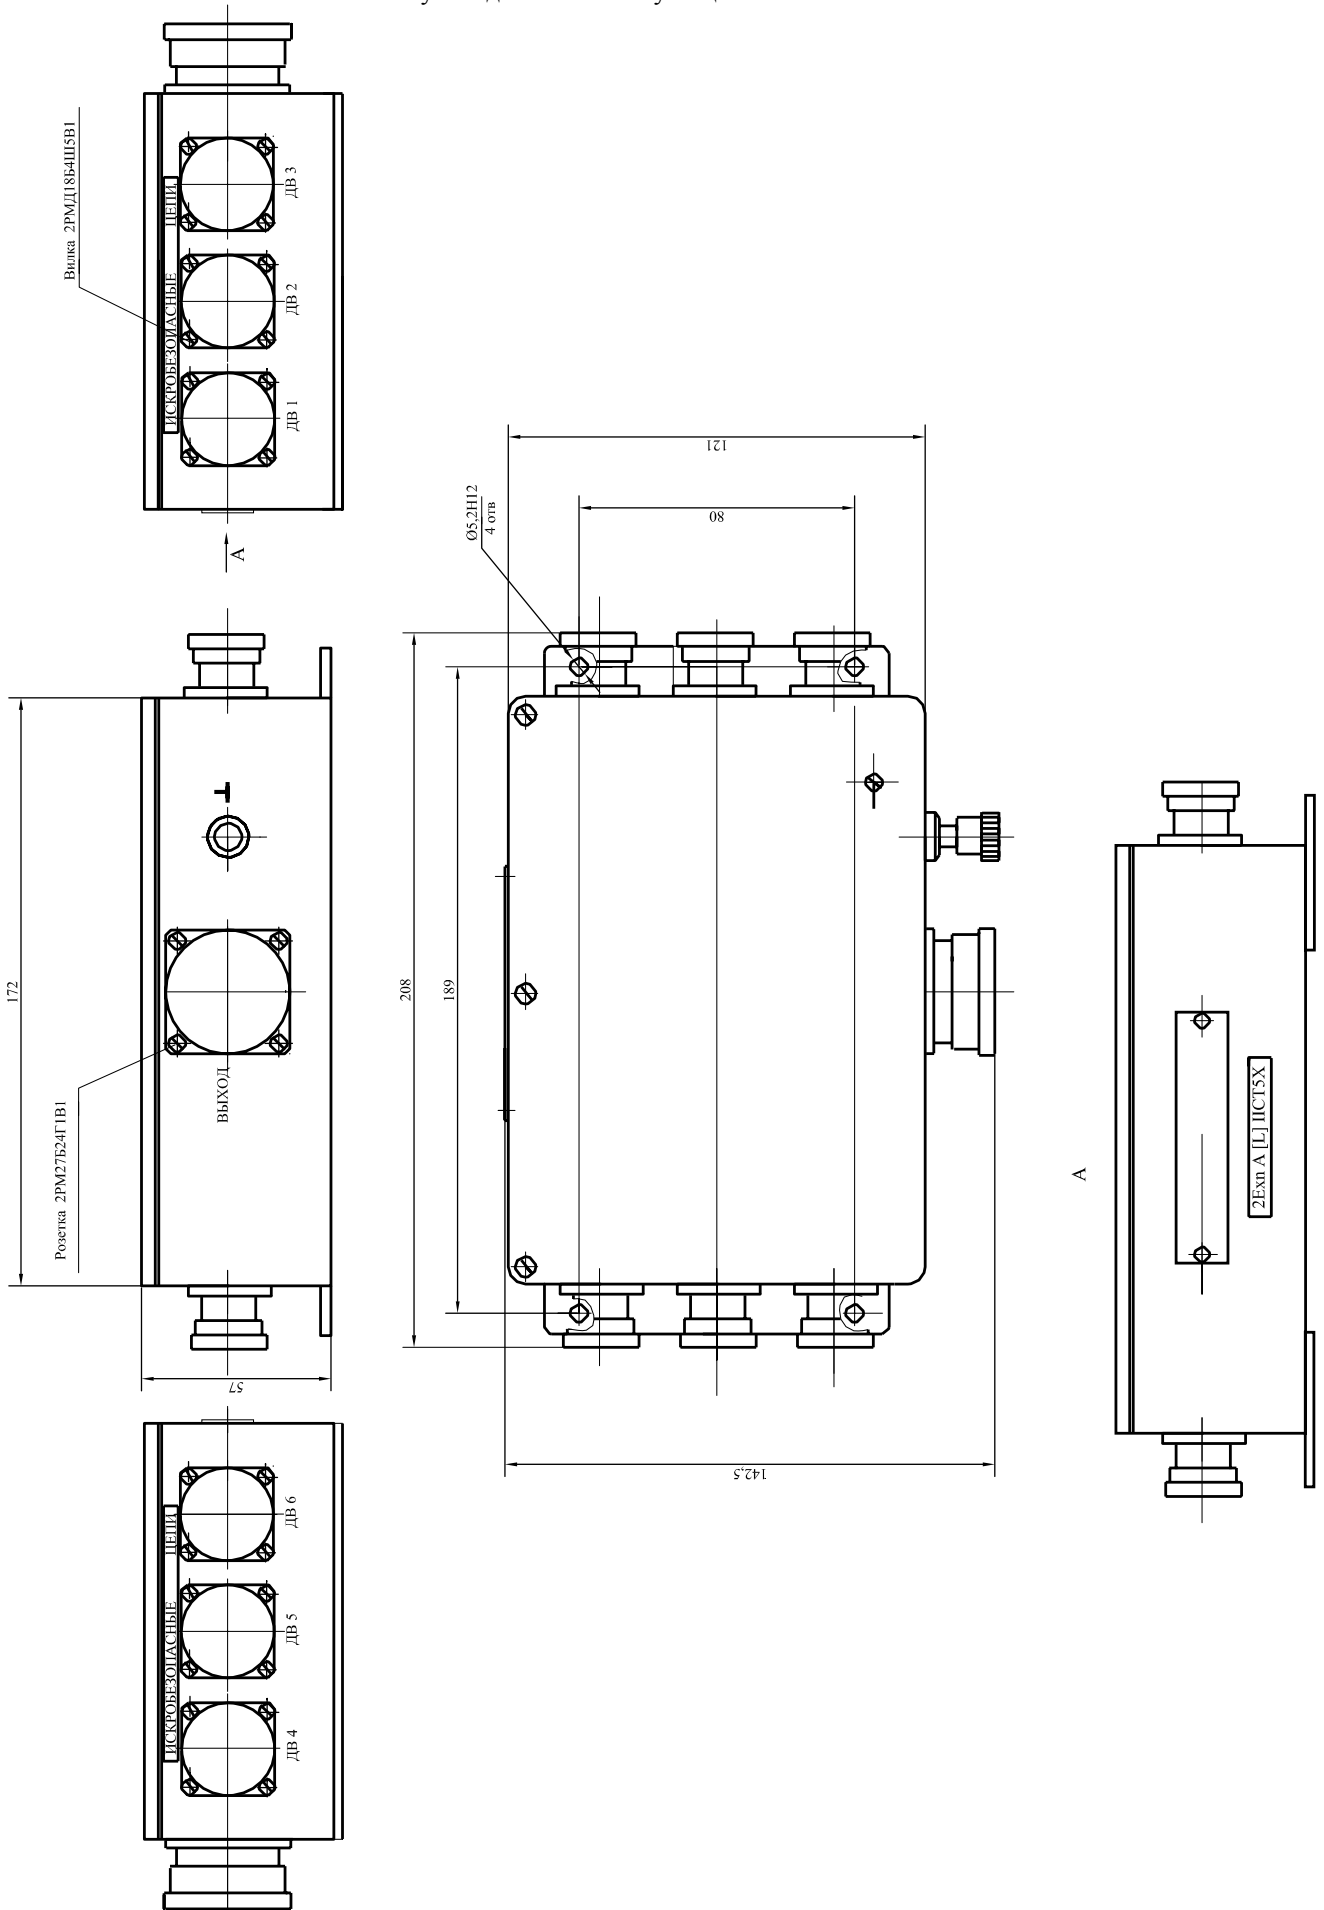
Габаритно-установочные размеры блока согласующего БС-16-45-6.1
